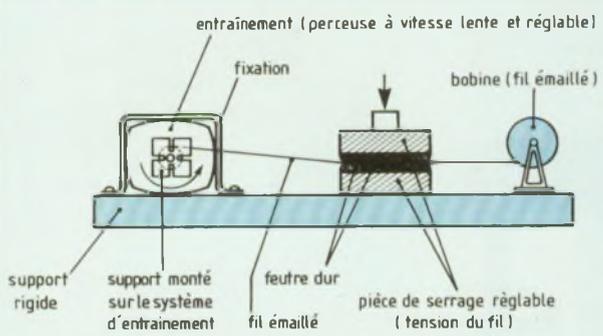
Procédé proposé pour le bobinage des selfs à air sur le support démontable décrit sur la figure 1.
